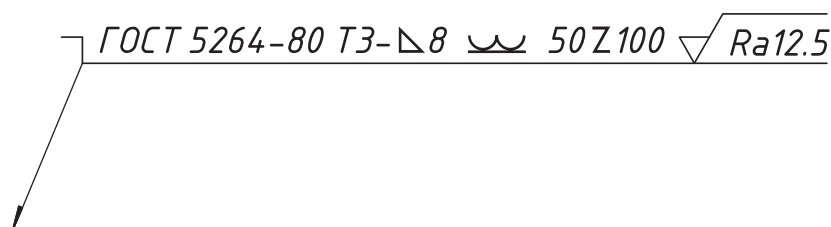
Пример условного обозначения сварного шва
